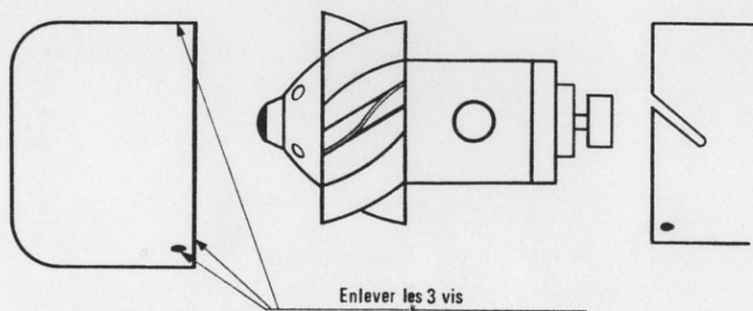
DÉMONTAGE DU MOTO-VENTILATEUR
